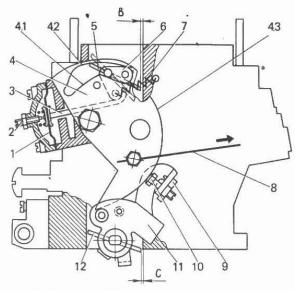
Dispositivo de arranque del carburador 21053-1107010:
